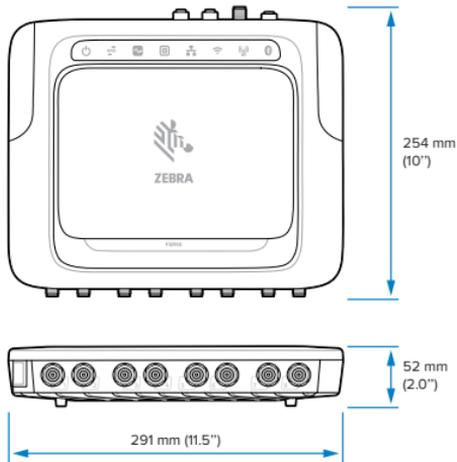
FXR90 – Mechanische Abmessungen mit Halterungen
